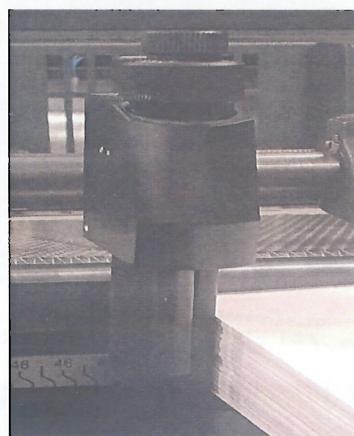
Регулировку подачи сжатого воздуха в боковых раздувателях.
